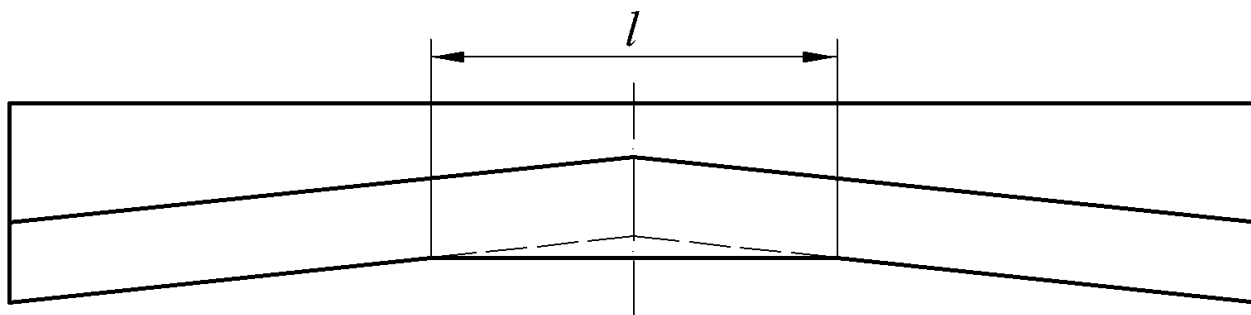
шеврон ніж зі складною формою ріжучої кромки конструкції «Северсталь» [54]
